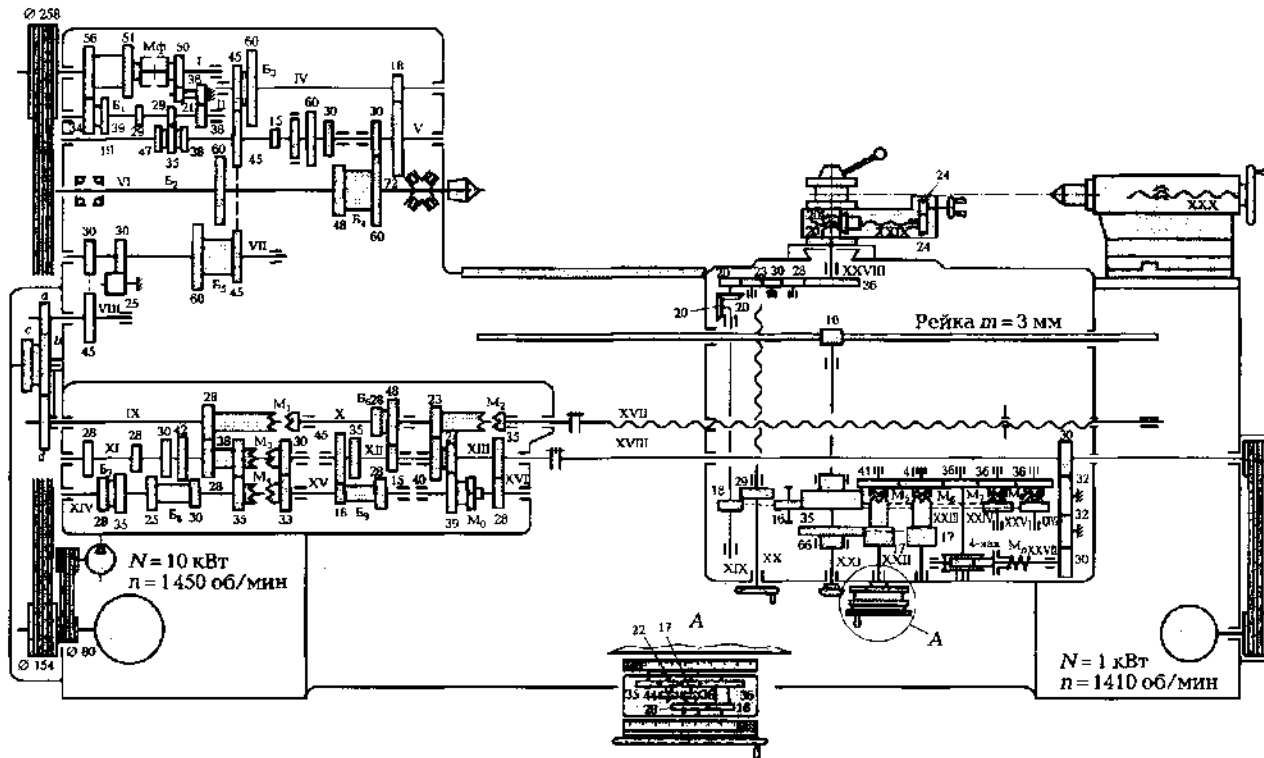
Кинематическая схема токарно-винторезного станка модели 16К20
